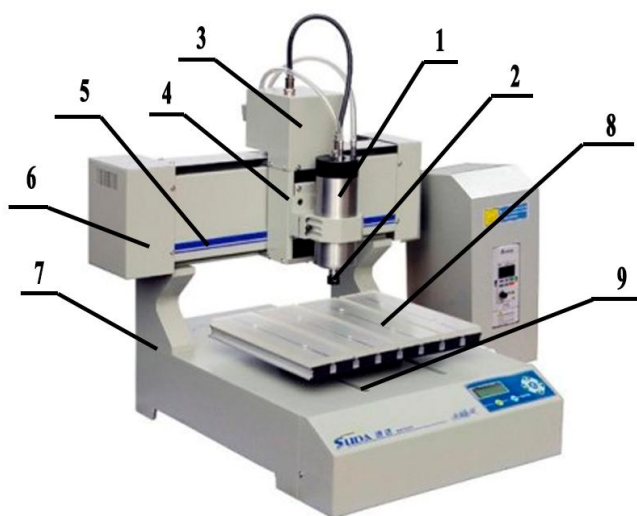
Фрезерний станок Suda SD-2616
